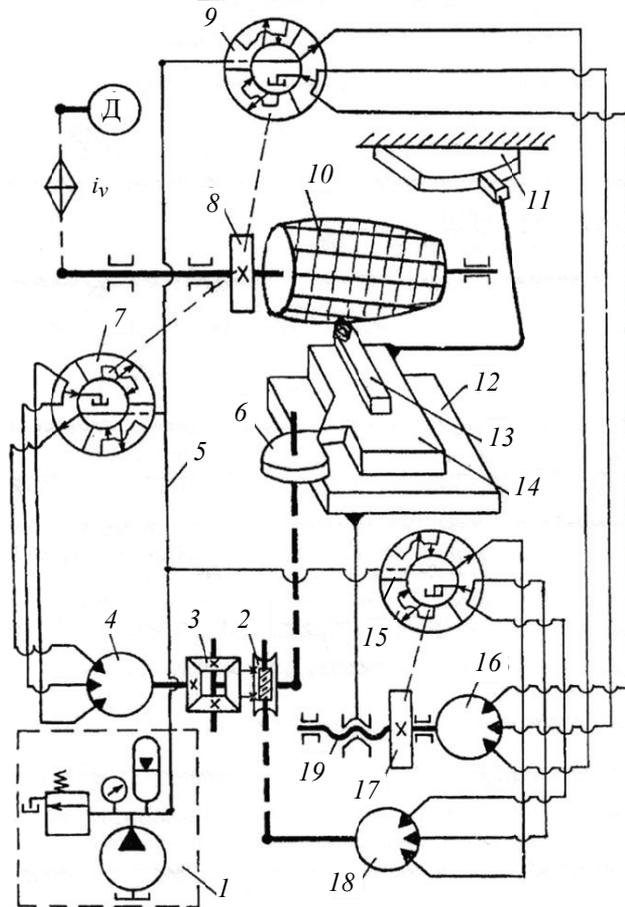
Структурная схема токарно-затыловочного станка с гидравлическими формообразующими связями
